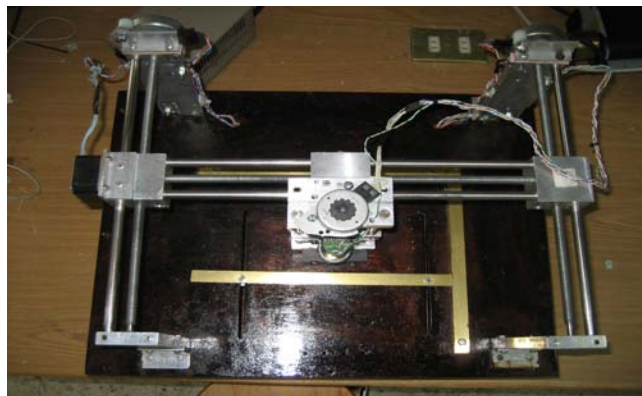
Sistema mecánico de perforación de tablilla de circuito impreso vista superior.
